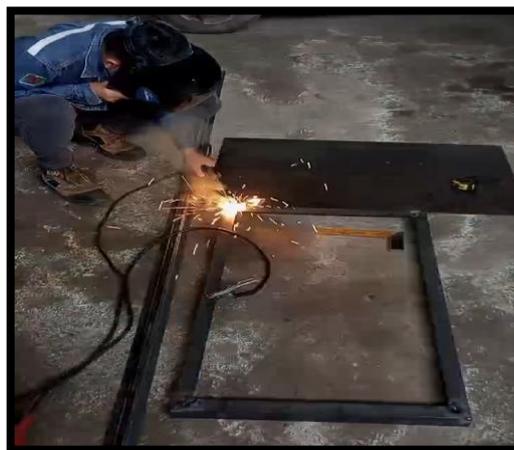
Creación del marco superior del banco de soldadura MIG.
